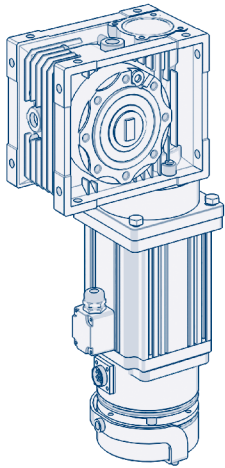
Порядок установки рычага расцепителя тормоза
